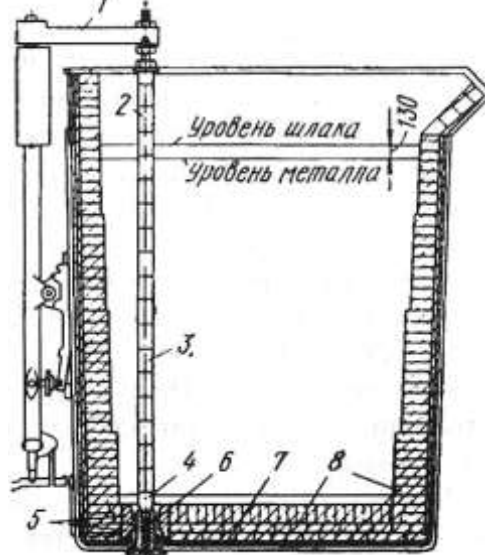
Сталеразливочный ковш со стопорным устройством:
